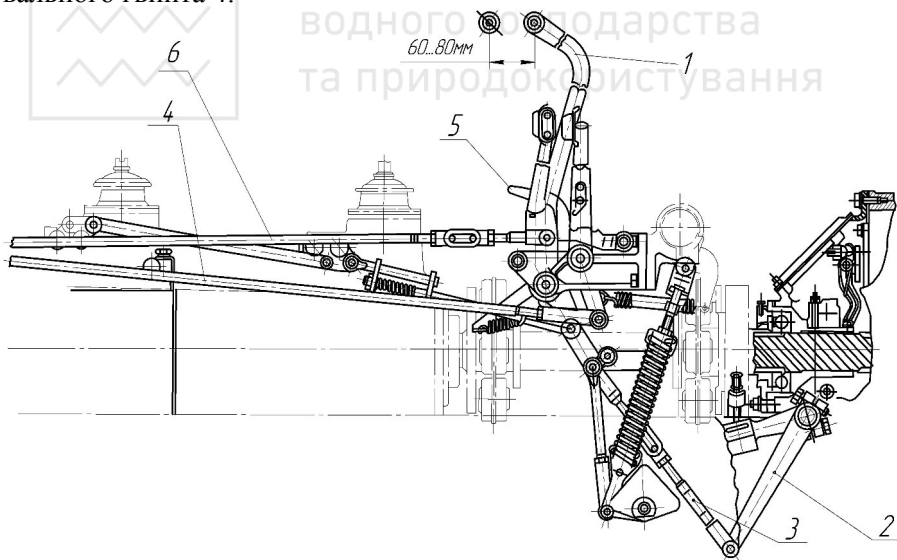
Механізм керування трактором ДТ-75: 1 - важіль керування гальмами планетарного механізму; 2 - важіль шліцьовий; 3 - тяга педалі муфти зчеплення; 4 - тяга педалі гальма; 5 - педаль гальма; 6 - тяга керування гальмами планетарного механізму повороту
